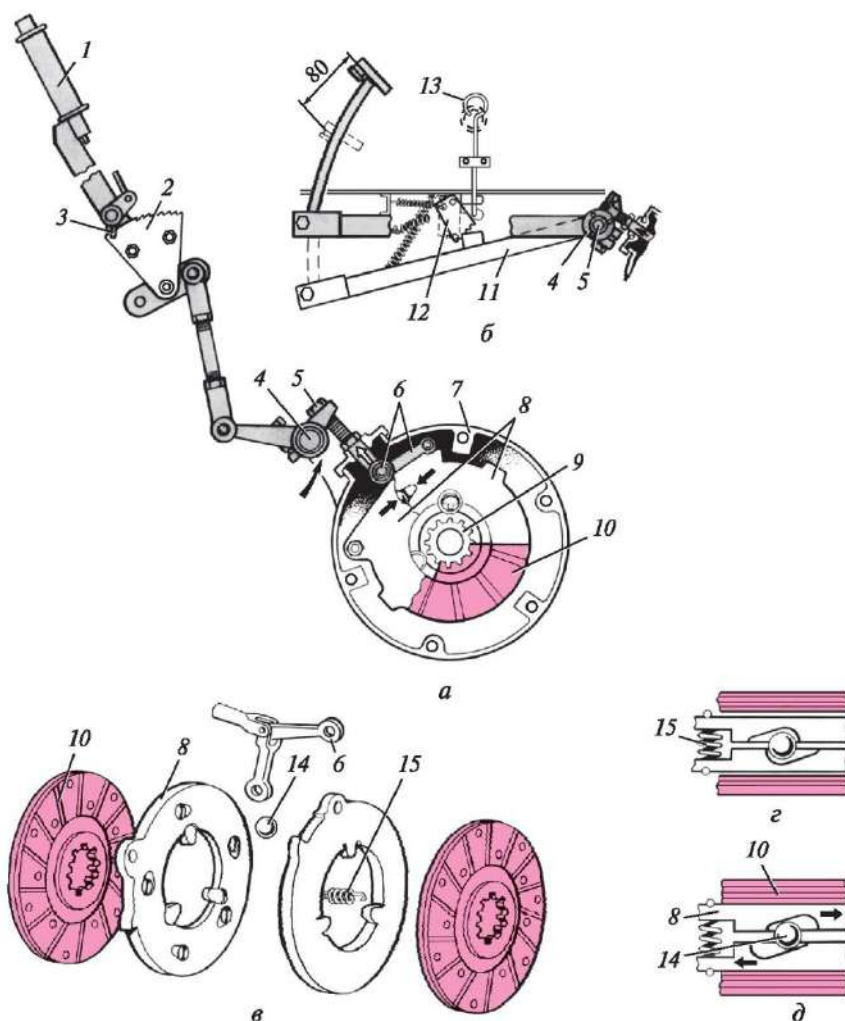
Тормоза дискового типа трактора МТЗ-80: а — стояночный; б — основной; в — составные части тормозного механизма; г, д — схемы тормоза в выключенном и включенном положениях; 1 — рычаг; 2 — зубчатый сектор; 3 — защелка рычага; 4 — ось промежуточного рычага педали; 5 — регулировочный болт; 6 — тяги; 7 — кожух; 8 — нажимные диски; 9 — хвостовик ведущей шестерни конечной передачи; 10 — соединительный диск; 11 — рычаг педали; 12 — защелка педали; 13 — тяга включения защелки педали; 14 — шарик; 15 — пружина; — движение деталей
